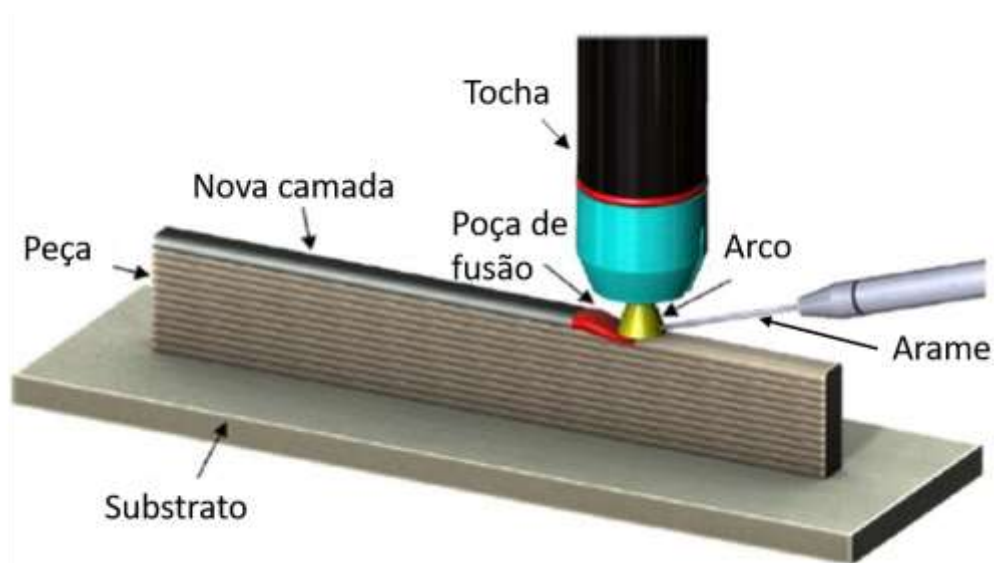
Processo de WAAM utilizando técnica de soldagem GTAW (RODRIGUES et al, 2019).
